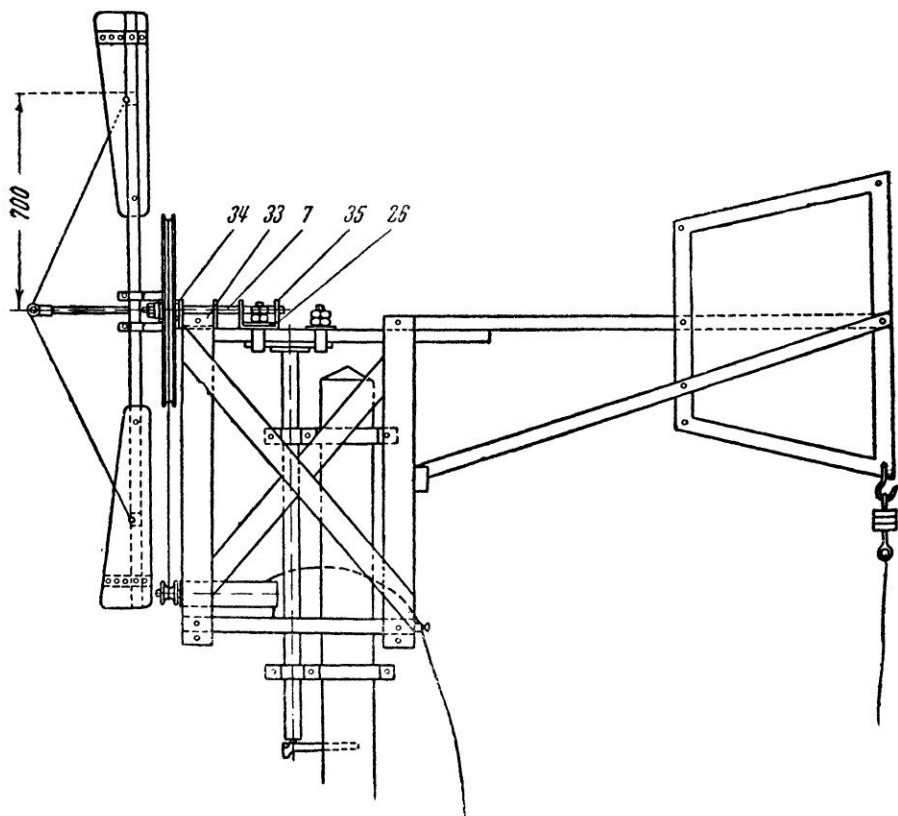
Боковой вид двухлопастного ветродвигателя КД-2:
